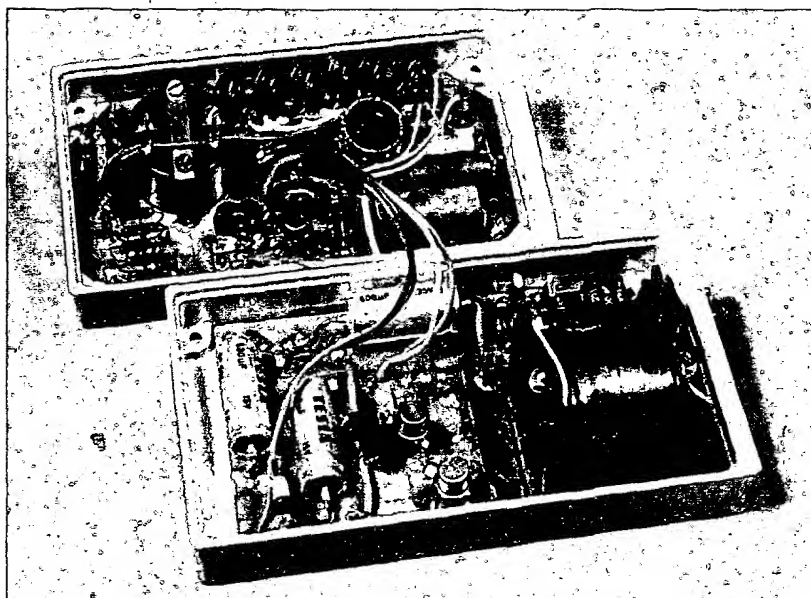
Rozložení součástek a deska A s plošnými spoji (P12)
